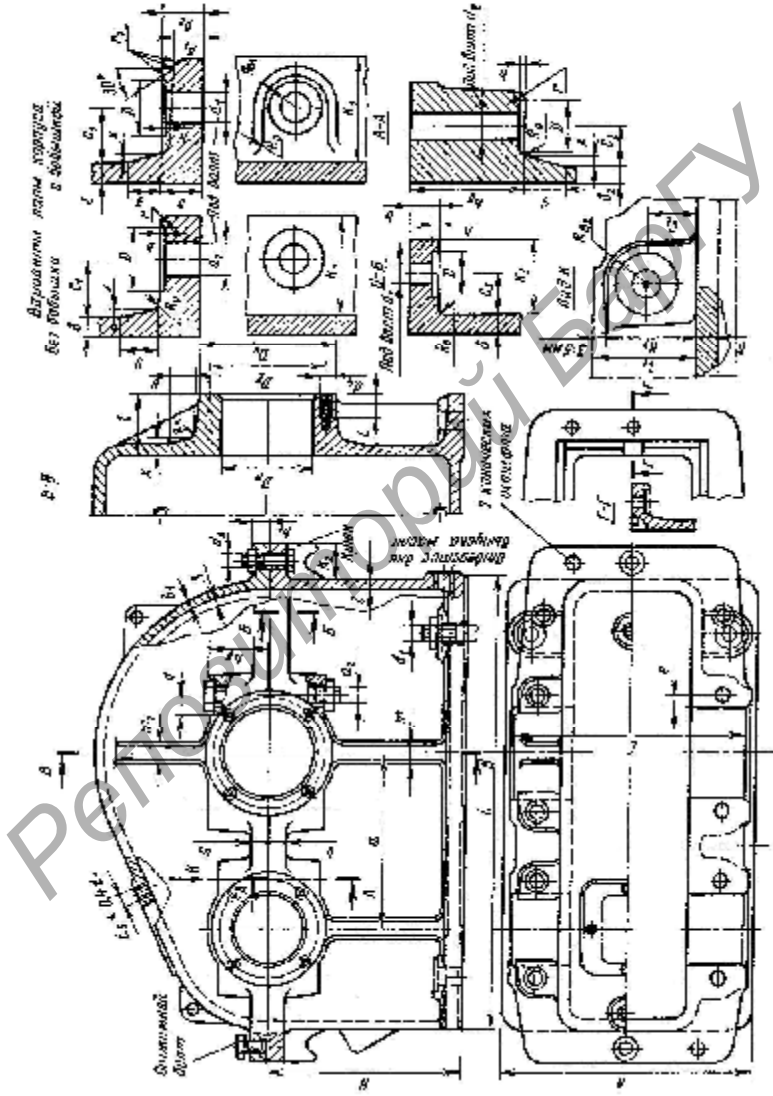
Конструктивные элементы корпуса редуктора
